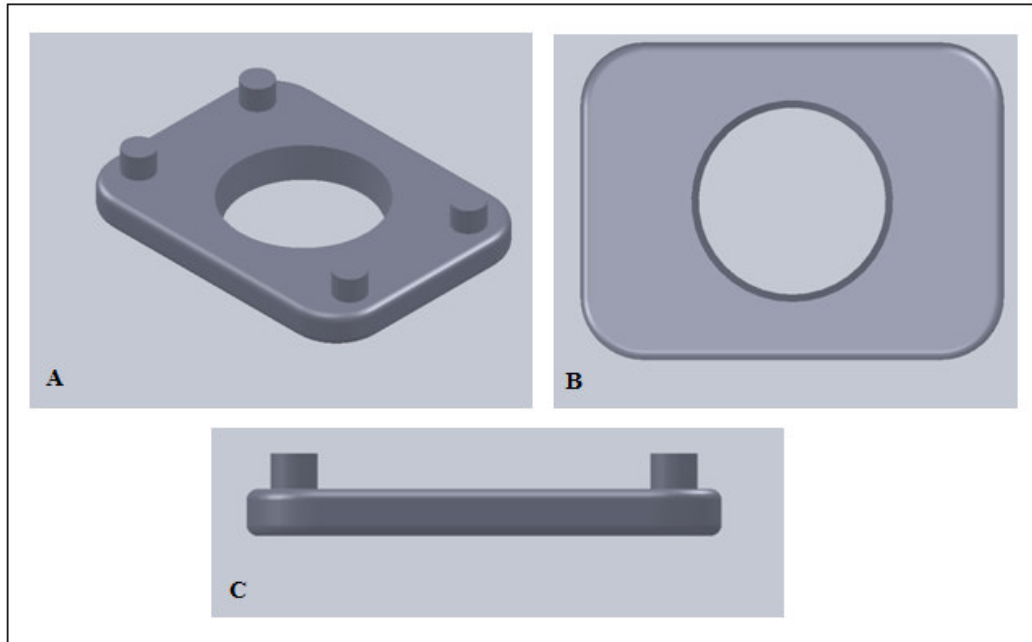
Fixador - Vista isométrica (A), frontal (B) e superior (C)
